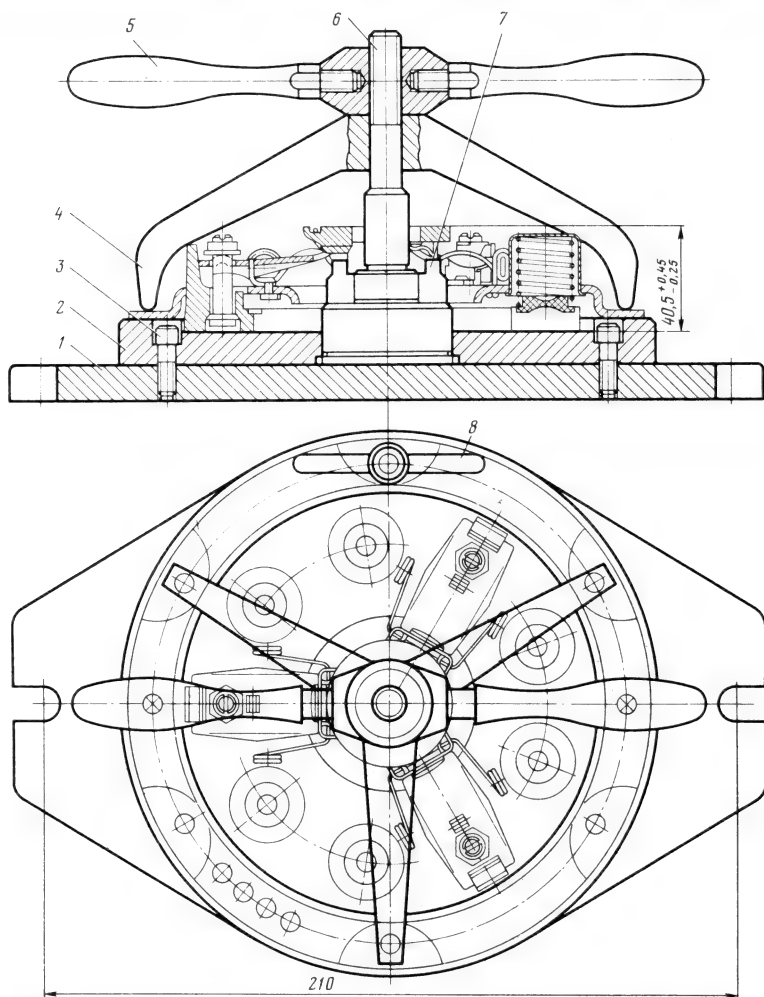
Приспособление для разработки и сборки муфты сцепления:
